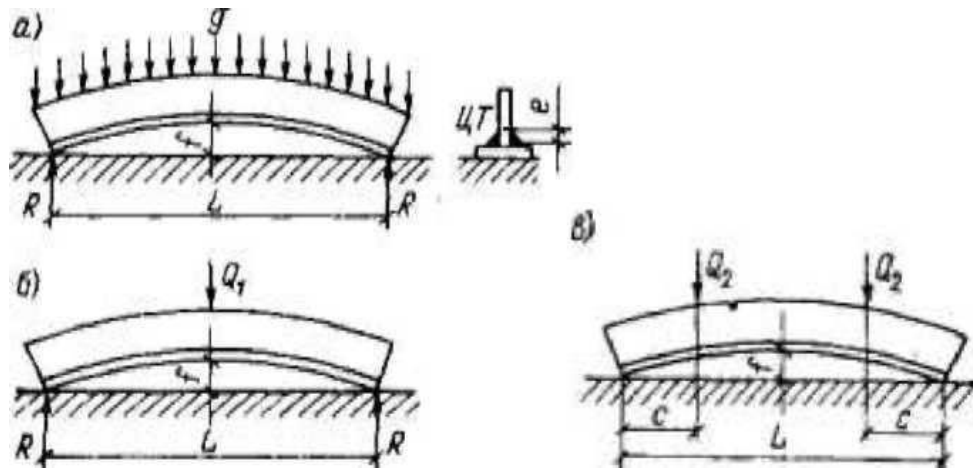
Продольная деформация сварной балки и схемы её нагружения в сборочно-сварочном кондукторе: *a* – равномерно распределённой нагрузкой в виде ряда клавишных прижимов; *б* – сосредоточенной силой посередине длины балки; *в* – двумя силами, симметрично расположенными по длине балки
